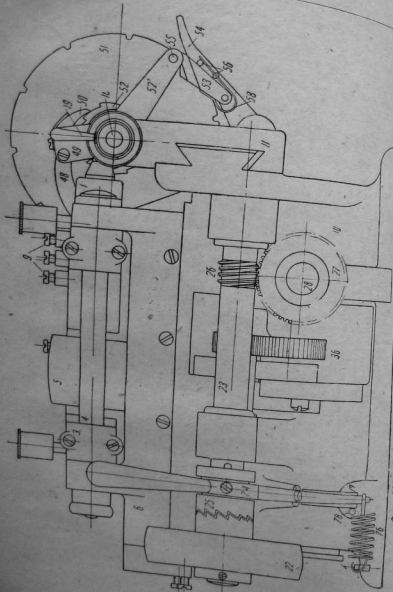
а. Триборезный полуавтомат 1-го часового завода (вид сбоку).
